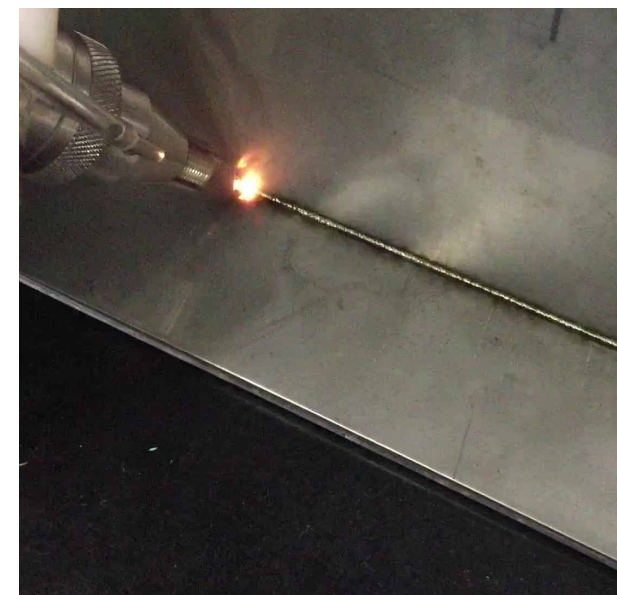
Пример лазерной сварки толстого металла
